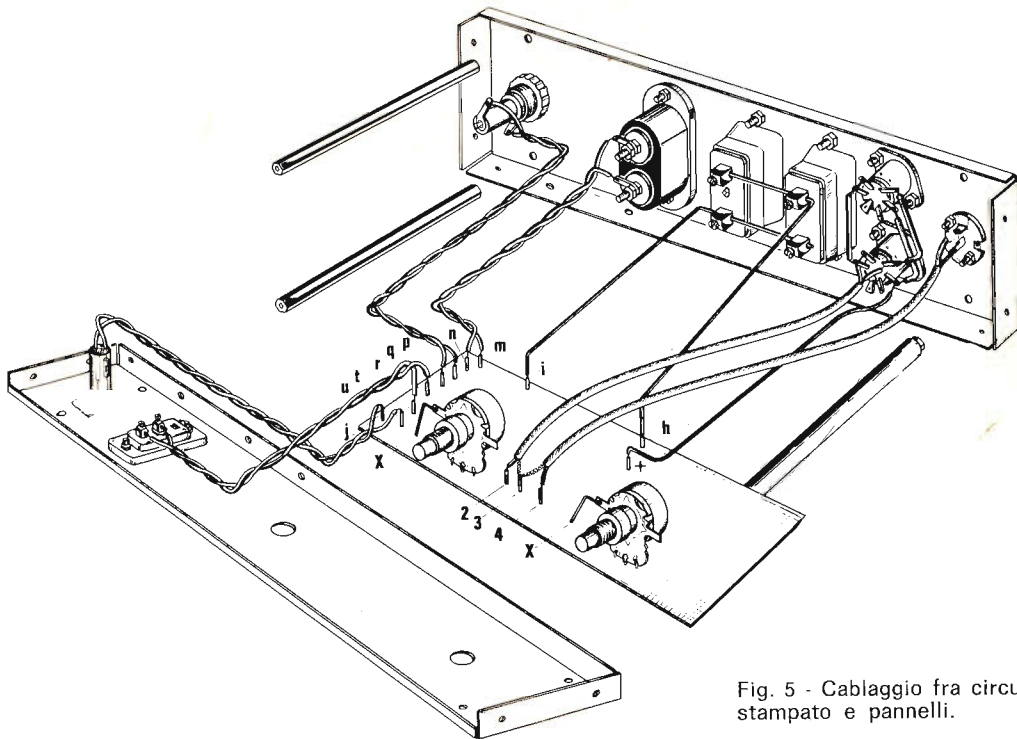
Cablaggio fra circuito stampato e pannelli.
